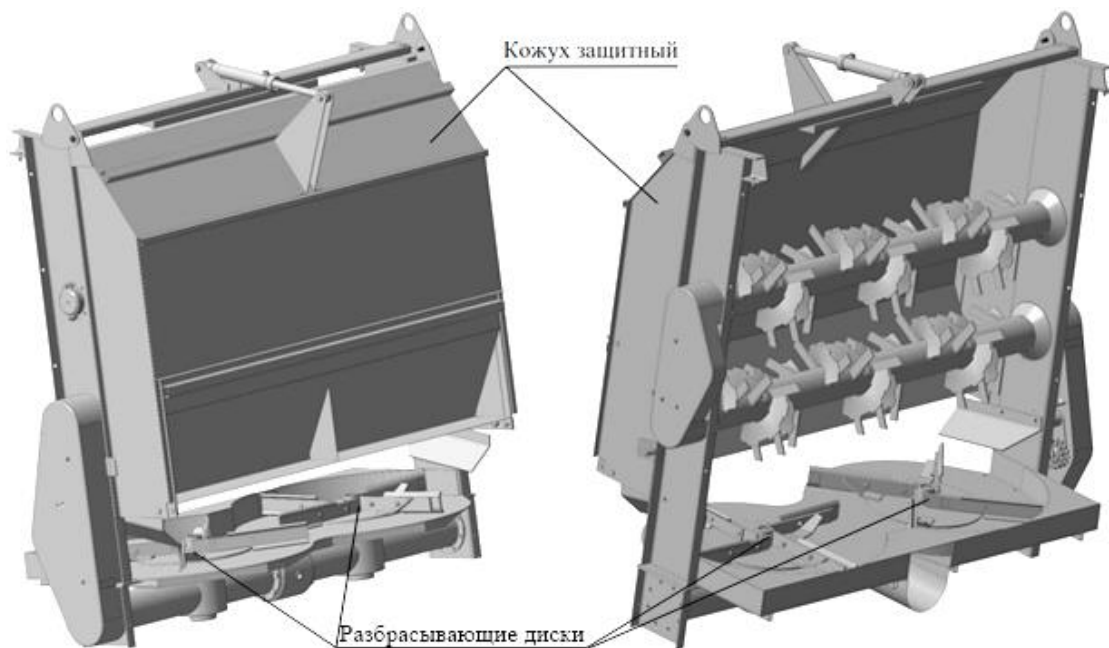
Защитный кожух и разбрасывающие диски распределительного устройства [93]
